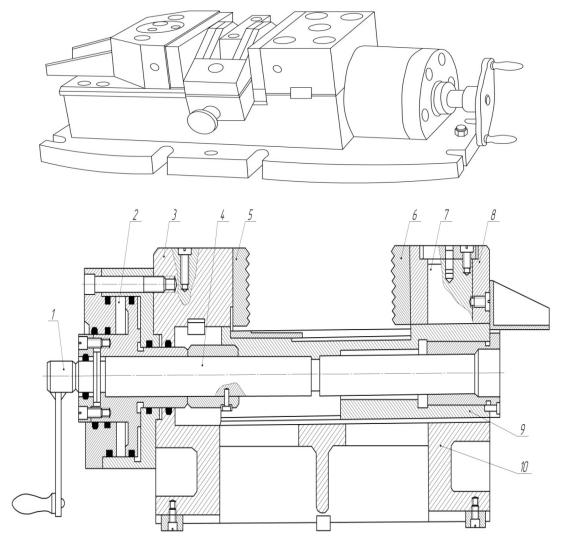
Тиски универсальные наладочные гидравлические: 1 — рукоятка; 2 — гидроцилиндр; 3 — неподвижная губка; 4 — винт; 5, 6 — сменные наладки; 7 — ось; 8 — поворотная губка; 9 — подвижная губка; 10 — корпус
